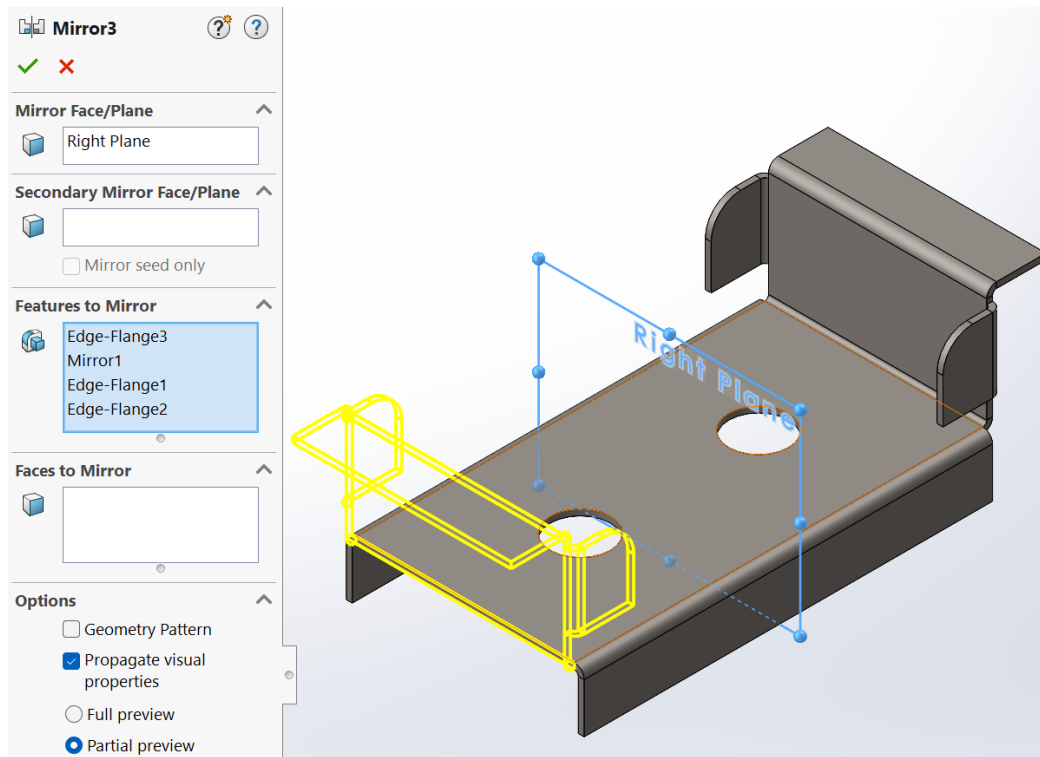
Завершення побудови деталі «Корпус»
